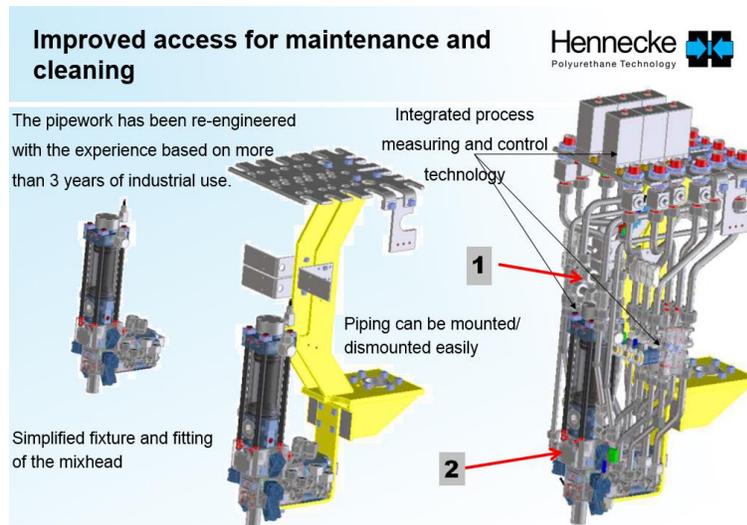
Cabezal de Mezcla de seis componentes, para montaje en robot.
